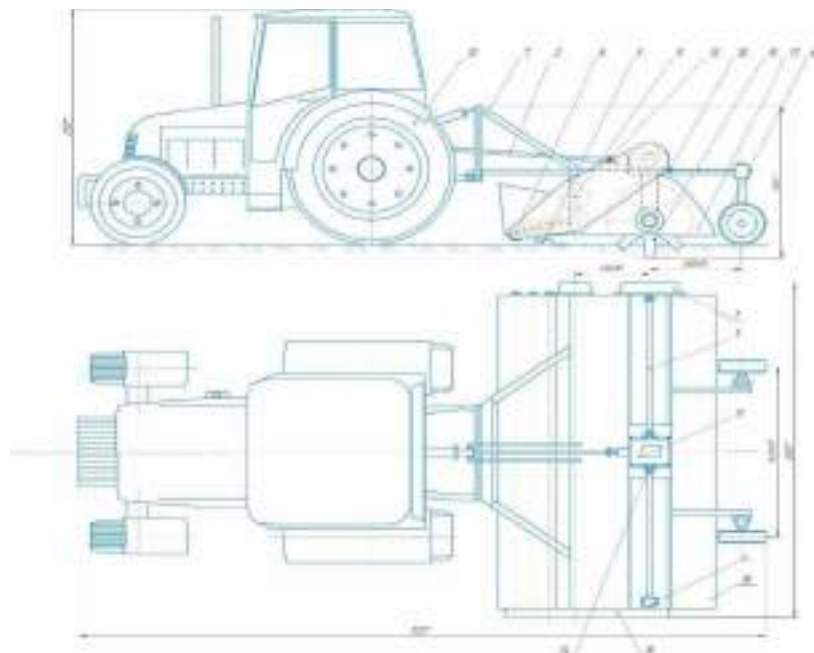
Проектна машина: 1 – Бортовий редуктор; 2 – вал карданний; 3 – вал поперечний; 4 – вузол підшипниковий; 5 – лижа; 6 – опорне колесо; 7 – навісний пристрій; 8 – подаючі вальці; 9 – подрібнювач; 10 – рама; 11 – редуктор конічний; 12 – трактор; 13 – муфта запобіжна; 14 – муфта з'єднувальна; 15 – фреза; 16 – щиток захисний; 17 – щиток боковий; 18 – щиток відбивний.
